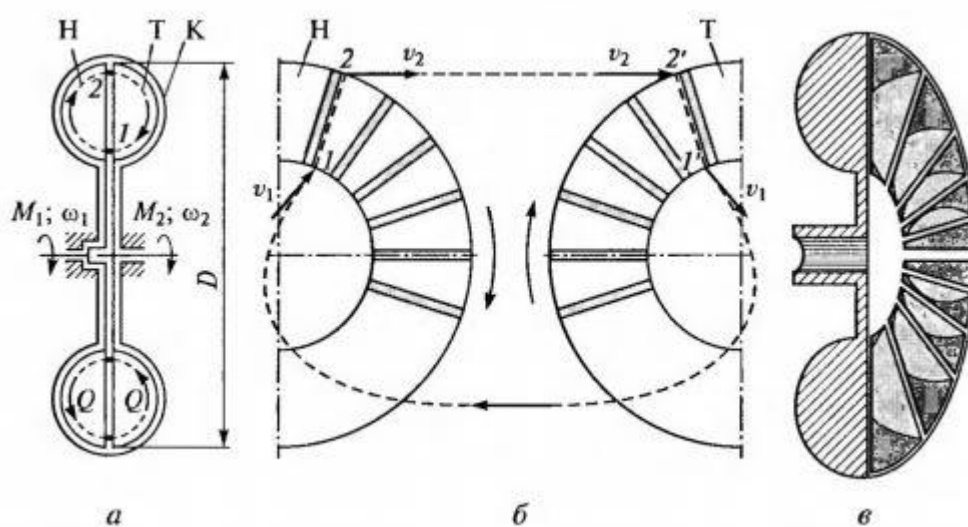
Конструктивная схема гидромуфты: а - осевой разрез; б - развертка лопастной системы; в - насосное колесо (в разрезе); Н - насосное колесо; Т - турбинное колесо; К – корпус.
